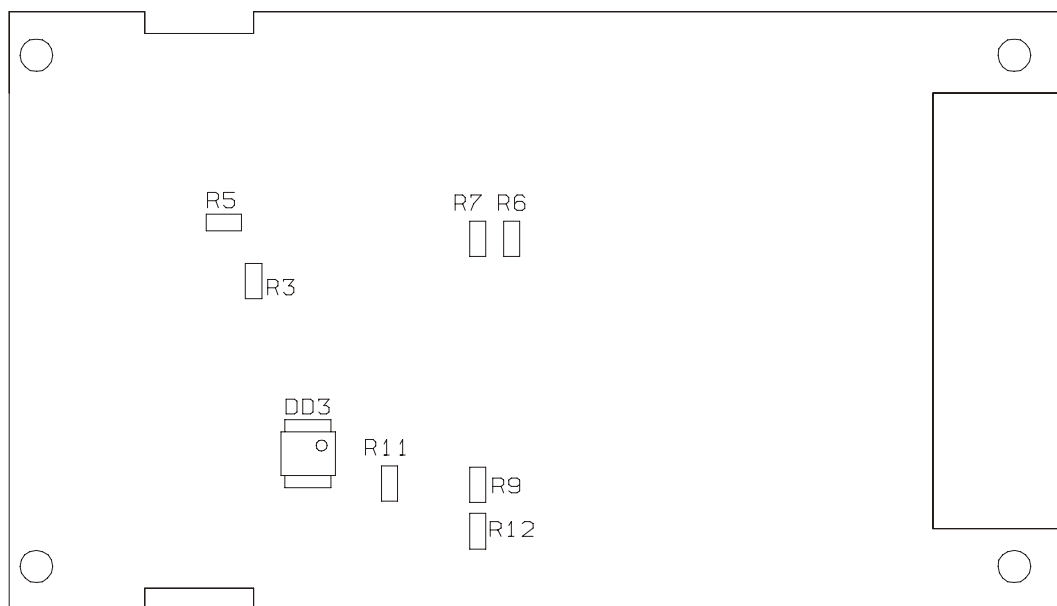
Сборочный чертеж платы обработки ФП11.3. Сторона пайки.
